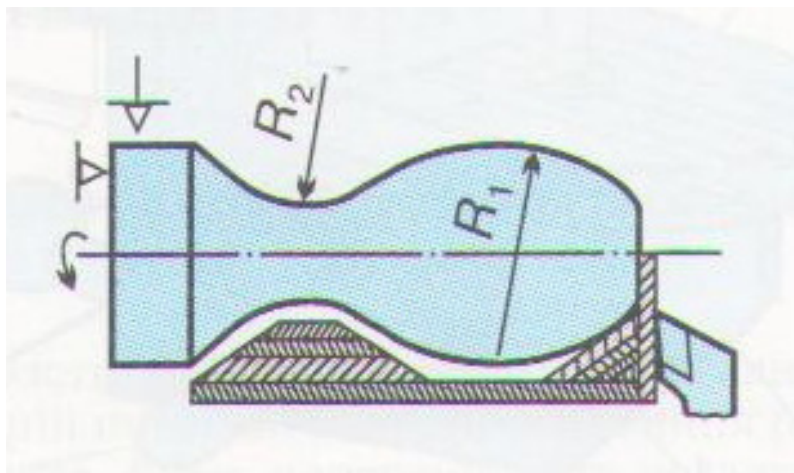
Попередня обробка заготовки фасонної деталі
